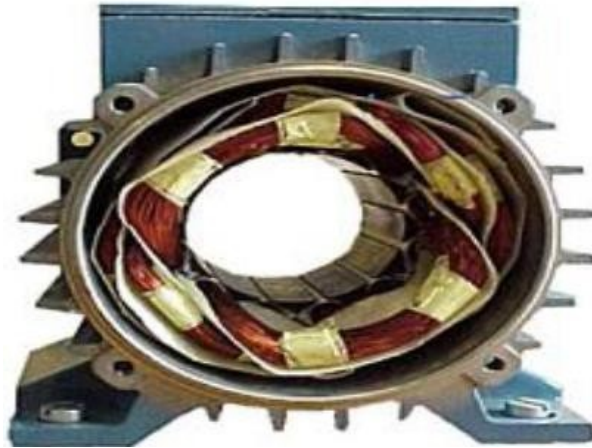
Stator d'un moteur asynchrone à cage
